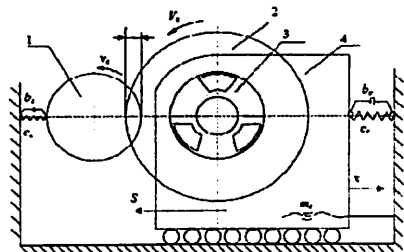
Схема круглошлифовального станка в виде трехмассовой модели
